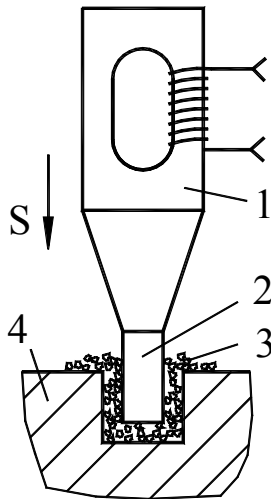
Схема ультразвуковой обработки: 1 – преобразователь; 2 – инструмент; 3 – абразив; 4 – заготовка
